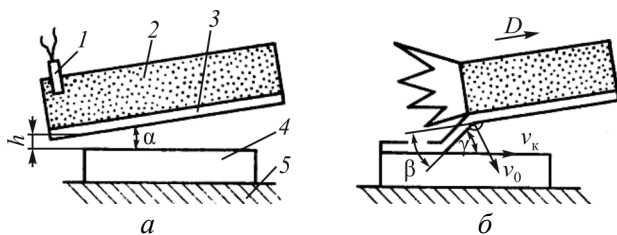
Схема сварки взрывом под углом: *a* – до взрыва; *б* – после взрыва
